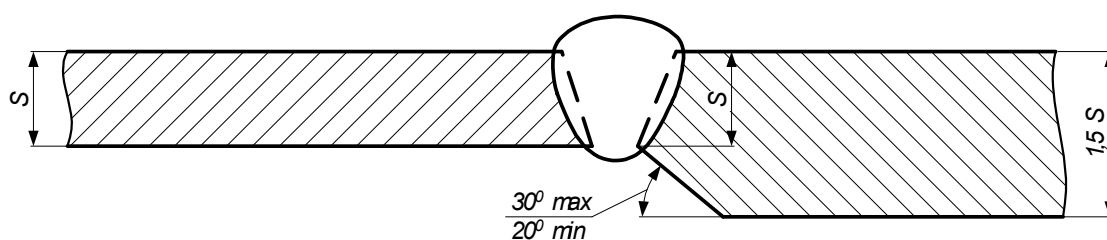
Конструктивные размеры разделки кромок и сварных швов разнотолщинных труб (до 1,5 толщины стенки)
